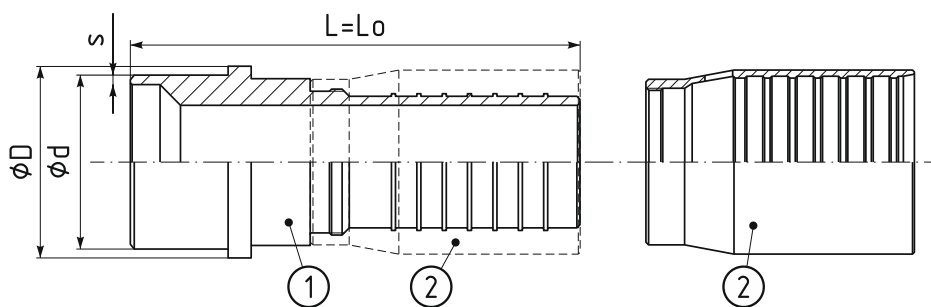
Фитинг обжимной под сварку
